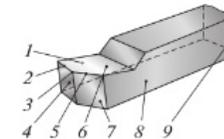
Основные части и элементы резца: 1 — головка; 2 — вспомогательная режущая кромка; 3 — вершина; 4 — задняя вспомогательная поверхность; 5 — главная режущая кромка; 6 — передняя поверхность; 7 — задняя главная поверхность; 8 — опорная поверхность; 9 — тело (стержень)
